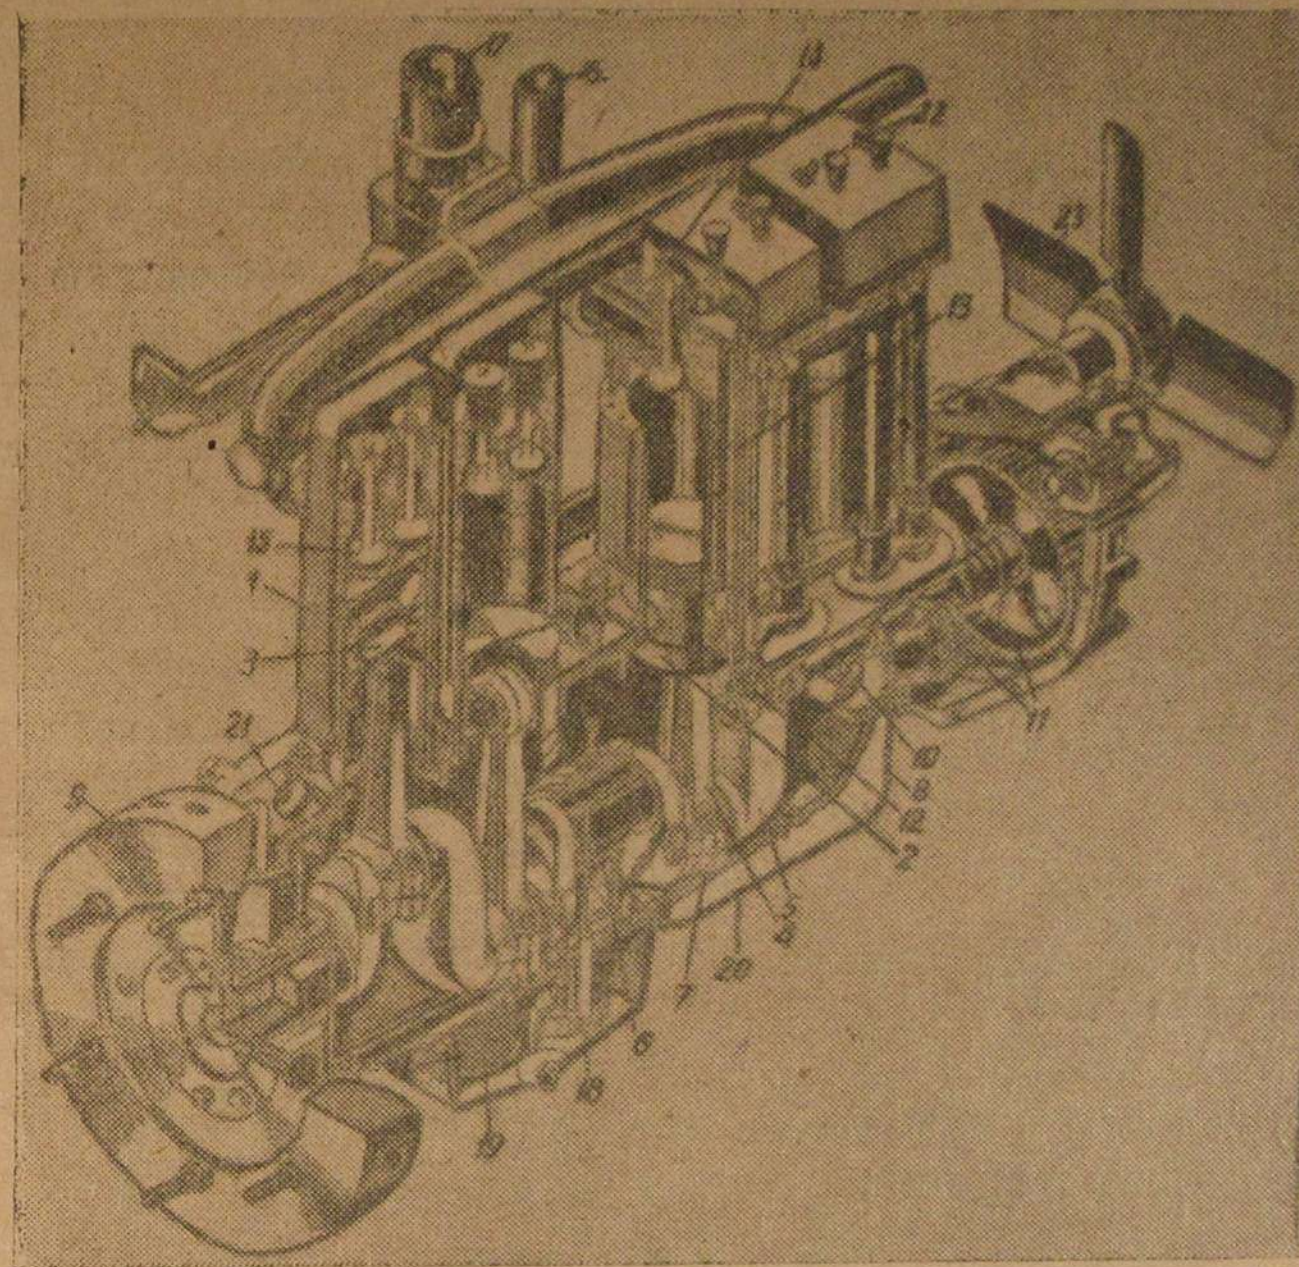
Двигатель ЧТЗ «Сталинец-60» в разрезе: 1 — цилиндр, 2 — поршень, 3 — поршневой палец, 4 — шатун, 5 — коленчатый вал, 6 — подшипник коренной, 7 — подшипник шатунный, 8 — картер, 9 — маховик, 10 — кулачковый вал, 11 — распределительные шестерни, 12 — толкатель, 13 — штанга, 14 — коромысло клапана, 15 — клапан, 16 — впускной трубопровод, 17 — выпускной трубопровод, 18 — масляный насос, 19 — масляный фильтр, 20 — маслопровод, 21 — масляный манометр, 22 — масленки для смазки коромысел, 23 — вентилятор.
